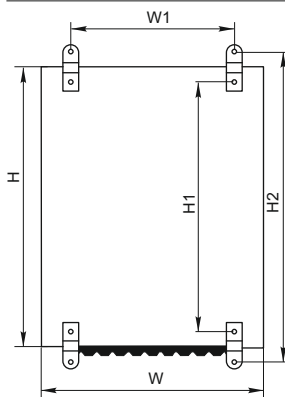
Вид корпуса сзади / Figure 1 – Enclosure back elevation / 1 сурет – Корпустың артқы көрінісі
